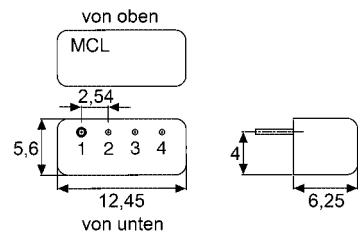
Gehäuse der TDC-xxx; ein blauer Ring auf der Unterseite markiert das Pin 1.
